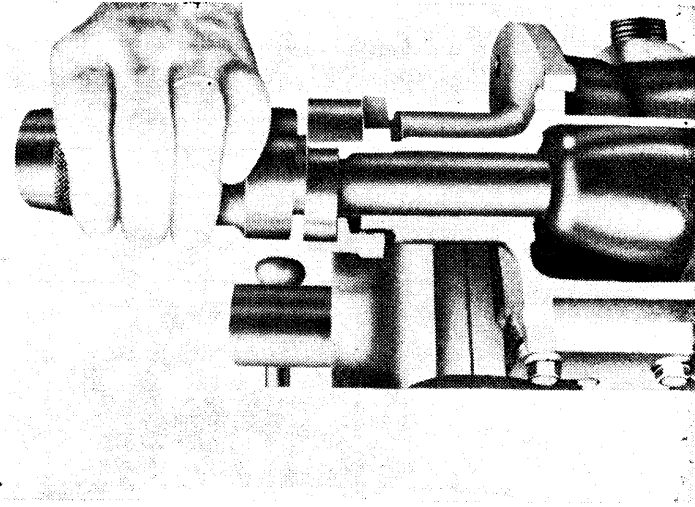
Einpressen der Wellendichtung in die Stopfbüchse mit der Vorrichtung D-56
